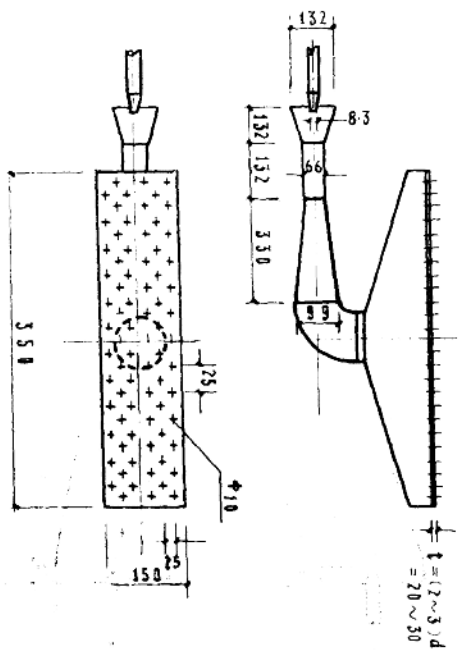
, 型 1 燃烧器外形尺寸 (结构图二)
